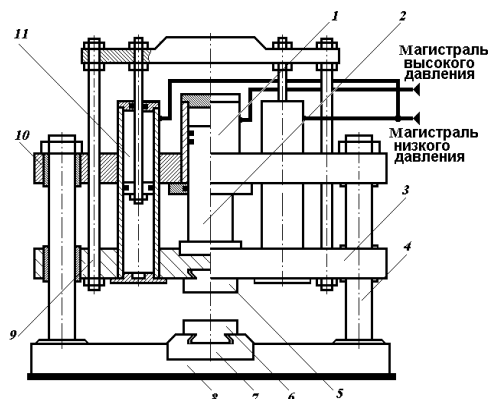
Ковочный гидравлический пресс: 1 – рабочий цилиндр; 2 – главный плунжер; 3 – подвижная поперечина; 4 – колонна; 5 – верхний боек; 6 – нижний боек; 7 – плита; 8 – нижняя неподвижная поперечина; 9 – тяга; 10 – верхняя неподвижная поперечина; 11 – цилиндр обратного хода.
